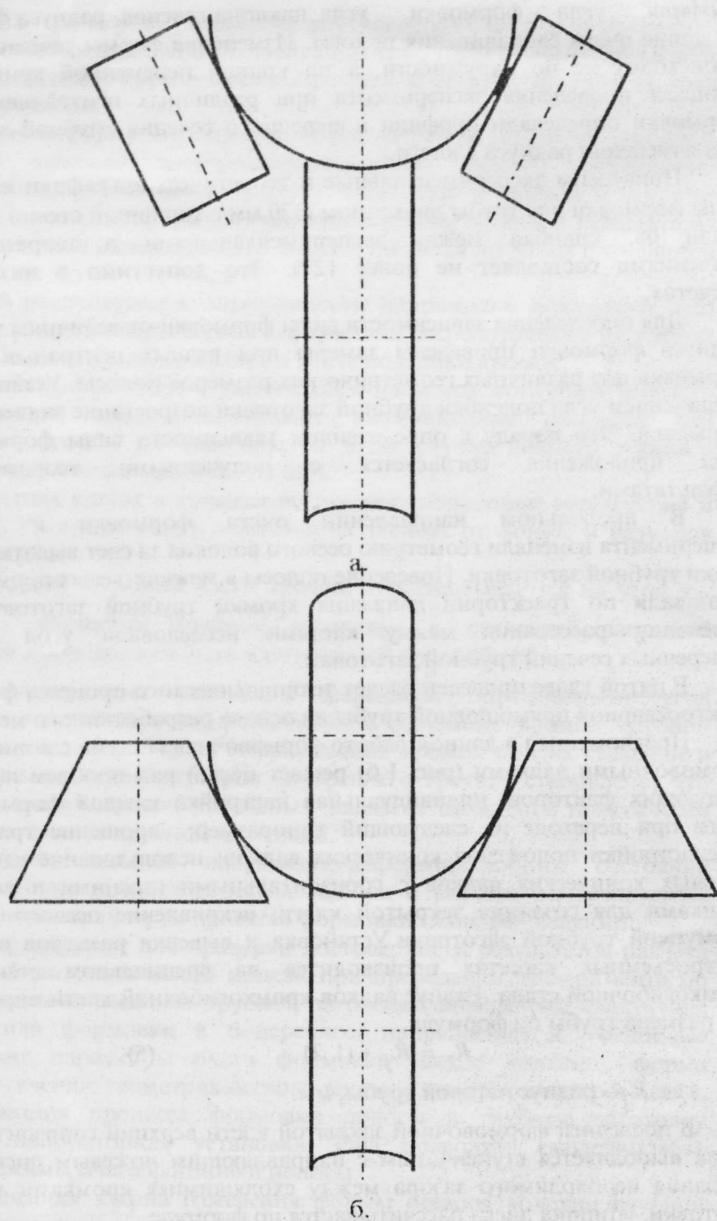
Формовочная клеть с гладкими валками открытого типа; а - существующая, б - предлагаемая.
